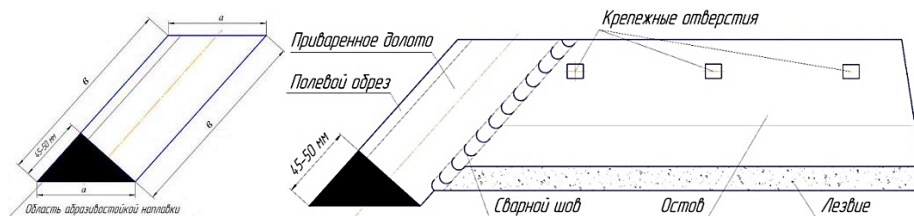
Штамповарной лемех с упрочненной заглабляющей частью
